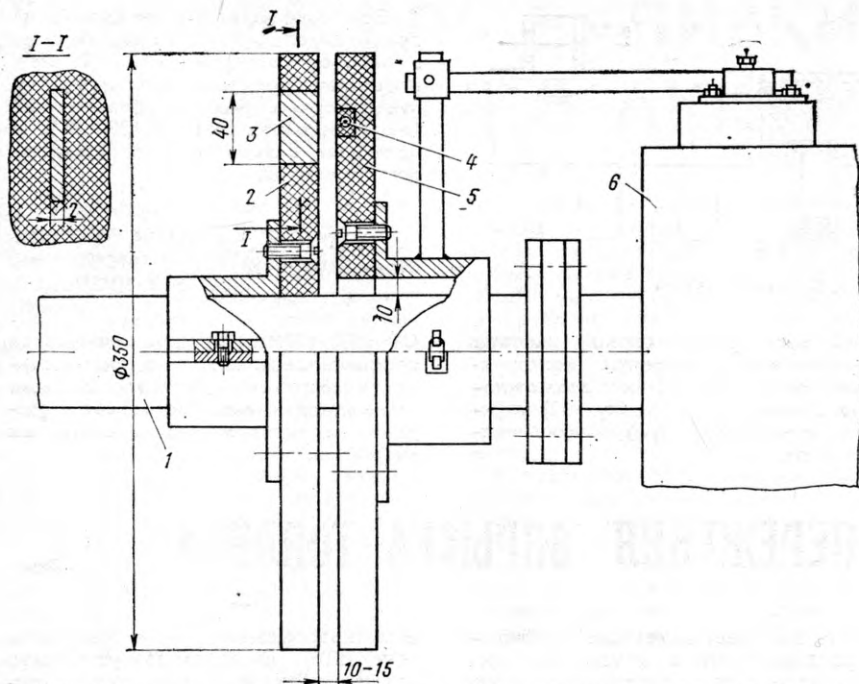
Крепление формирователя синхронимпульсов относительно вала отбора мощности: 1 — вал отбора мощности; 2 — подвижной диск; 3 — постоянный магнит; 4 — магнитоуправляемый контакт; 5 — неподвижный диск; 6 — корпус гидромеханического редуктора
